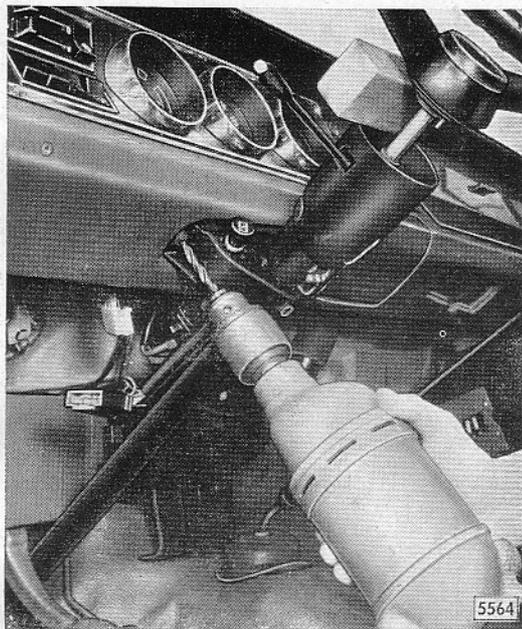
Schraubenkopf der Abreißschraube abbohren
